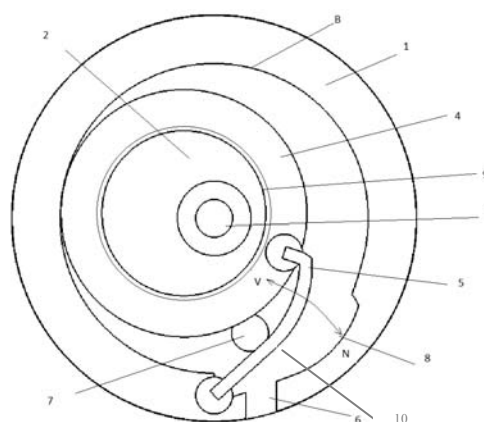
Роторный компрессор: 1 - корпус с внутренней цилиндрической рабочей поверхностью В, 2 - ротор цилиндрической формы, 3 – приводной вал, 4 - полый цилиндр, 5 - сборная заслонка, имеющая форму изогнутой пластины, 6 и 7 - впускное и выпускное окна, 8 - вырез корпуса, 9 – подшипник, 10 - заслонка
